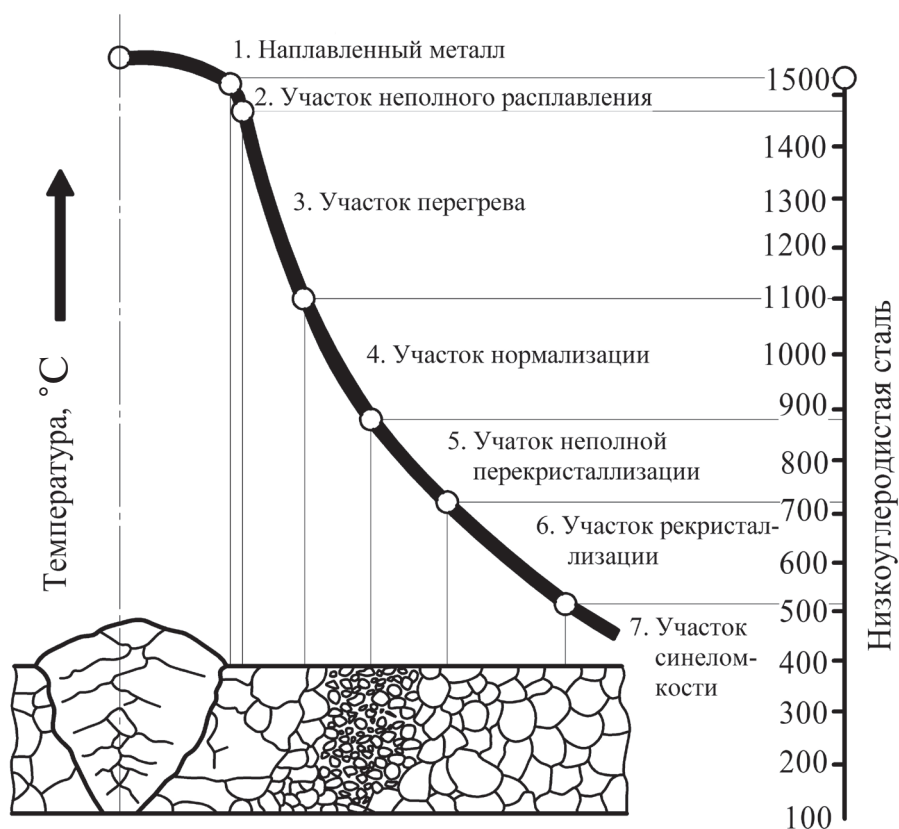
Структура металла шва и околошовной зоны после сварки оплавлением
